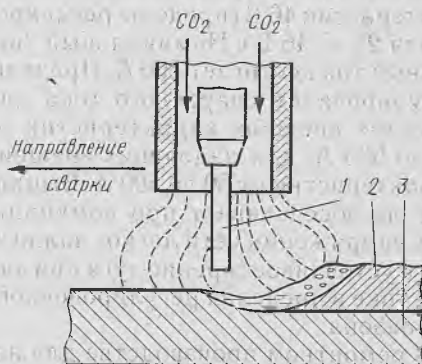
Схема сварки (наплавки) в среде углекислого газа:
